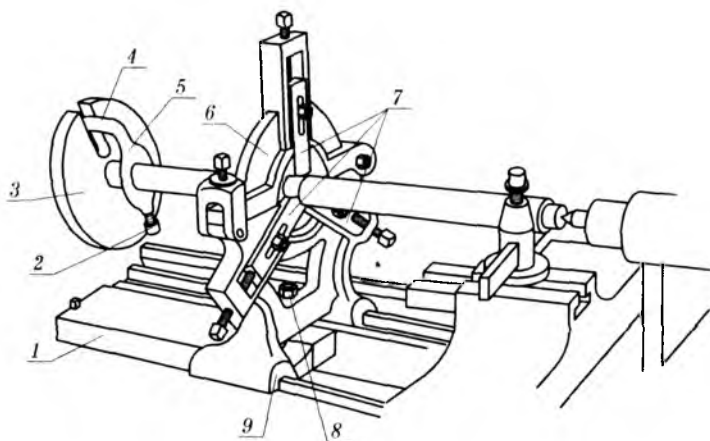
Обработка заготовки с применением неподвижного люнета:
